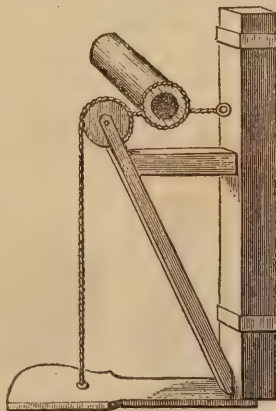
Machine à pédale pour serrer les charges d'artifice.
